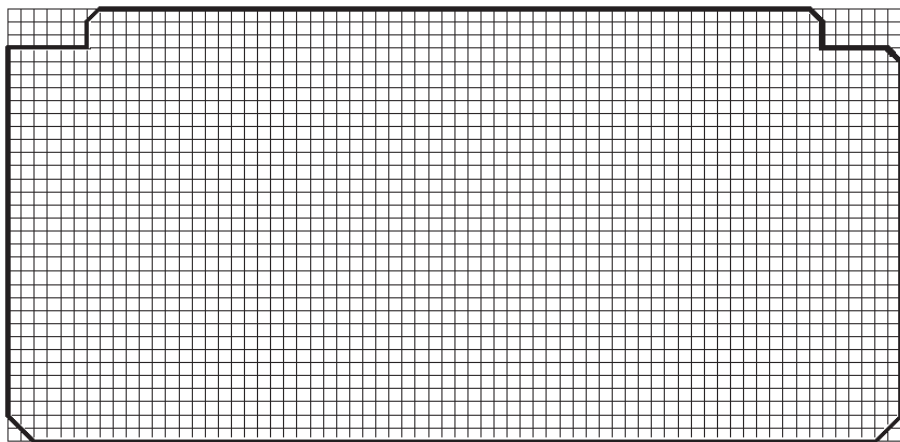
Заготовка печатной платы УБНК1 170×75 мм
